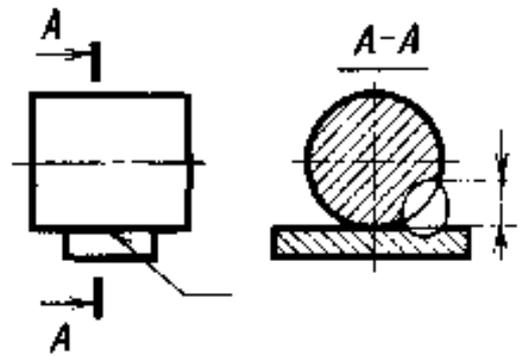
Условное изображение и обозначение нестандартного шва сварного соединения (шов соединения без скоса кромок, односторонний, выполняемый ручной электродуговой сваркой при монтаже изделия)
